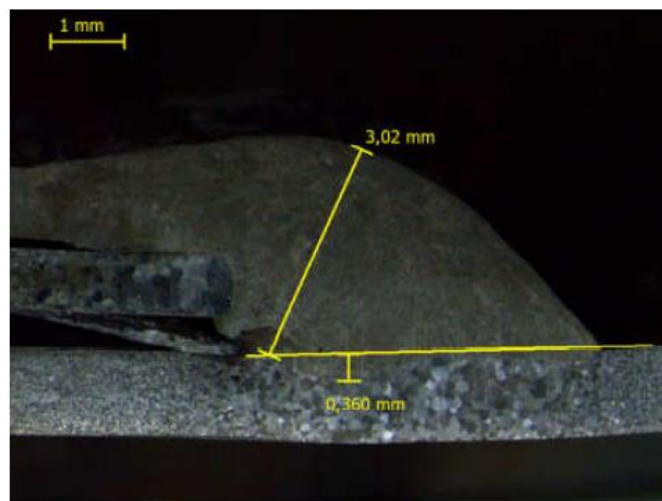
Macrografia do ponto 8 com soldadura circular mais fina (Penetração de 0,360mm)
